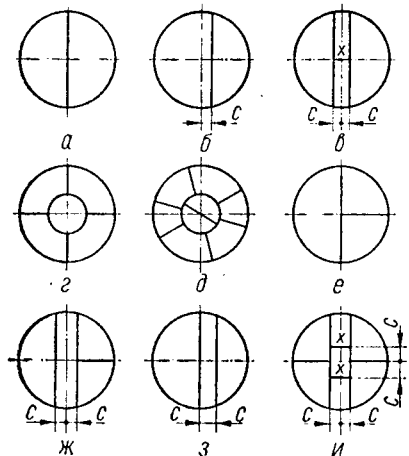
Схема расположения сварных швов при изготовлении эллиптических днищ.
